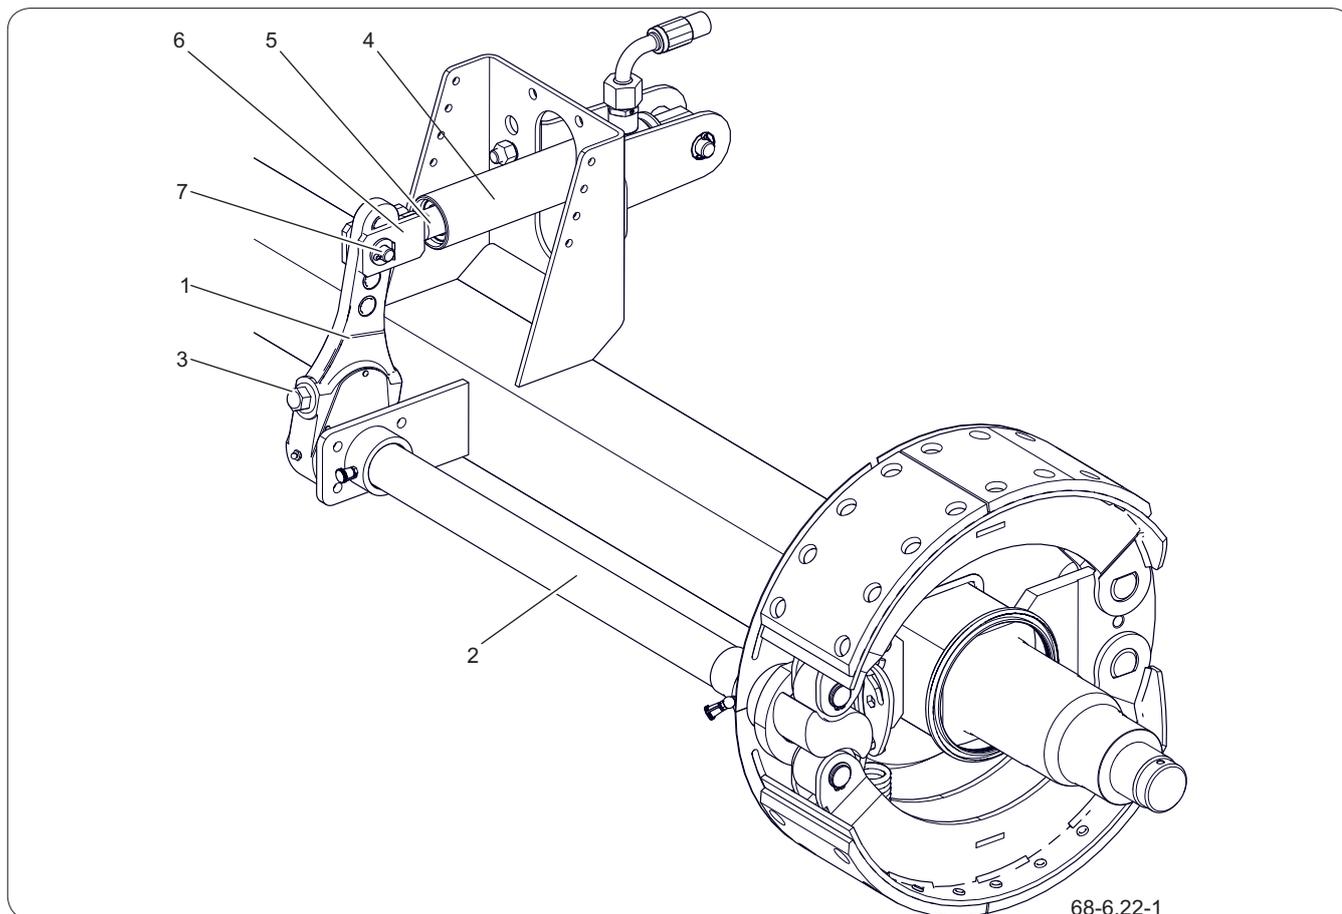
Aufbau einer hydraulischen Antriebsachsenbremse
